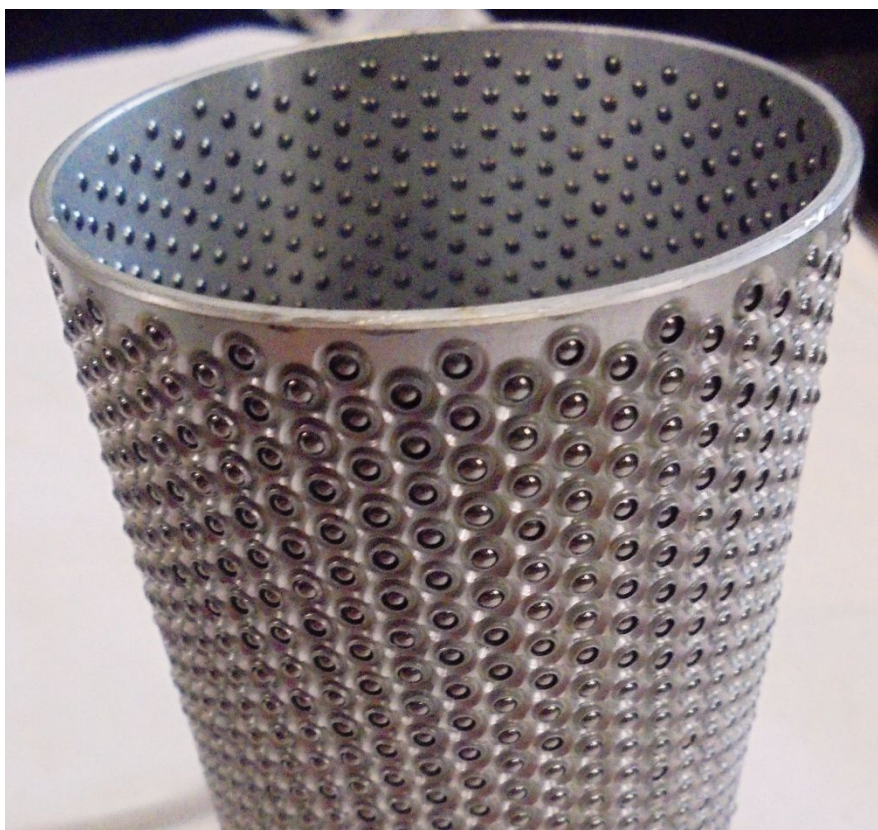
Detail demontovaného svazku tlumících planžet (č. 14 na rozpadu sestavy tlumiče)
